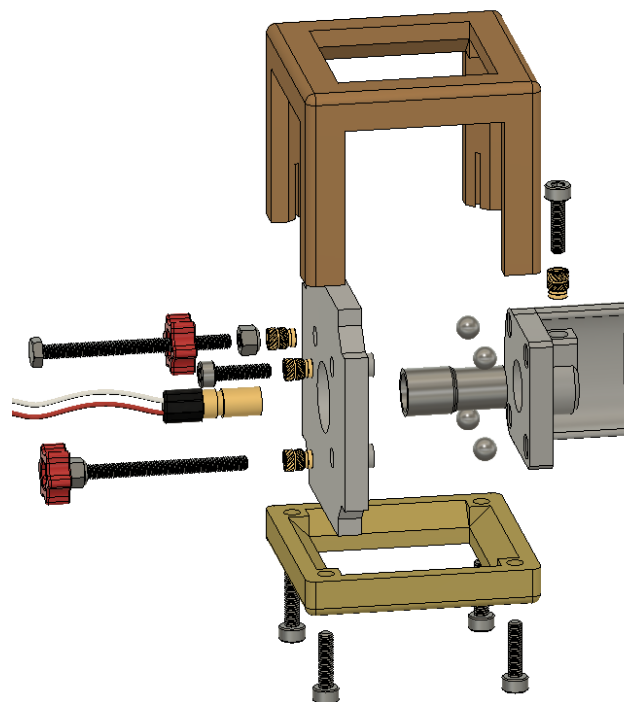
Explosionsansicht des Laserdioden-Würfels
